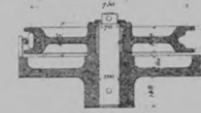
Poulie de bajoyer de la chaîne de fermeture.
